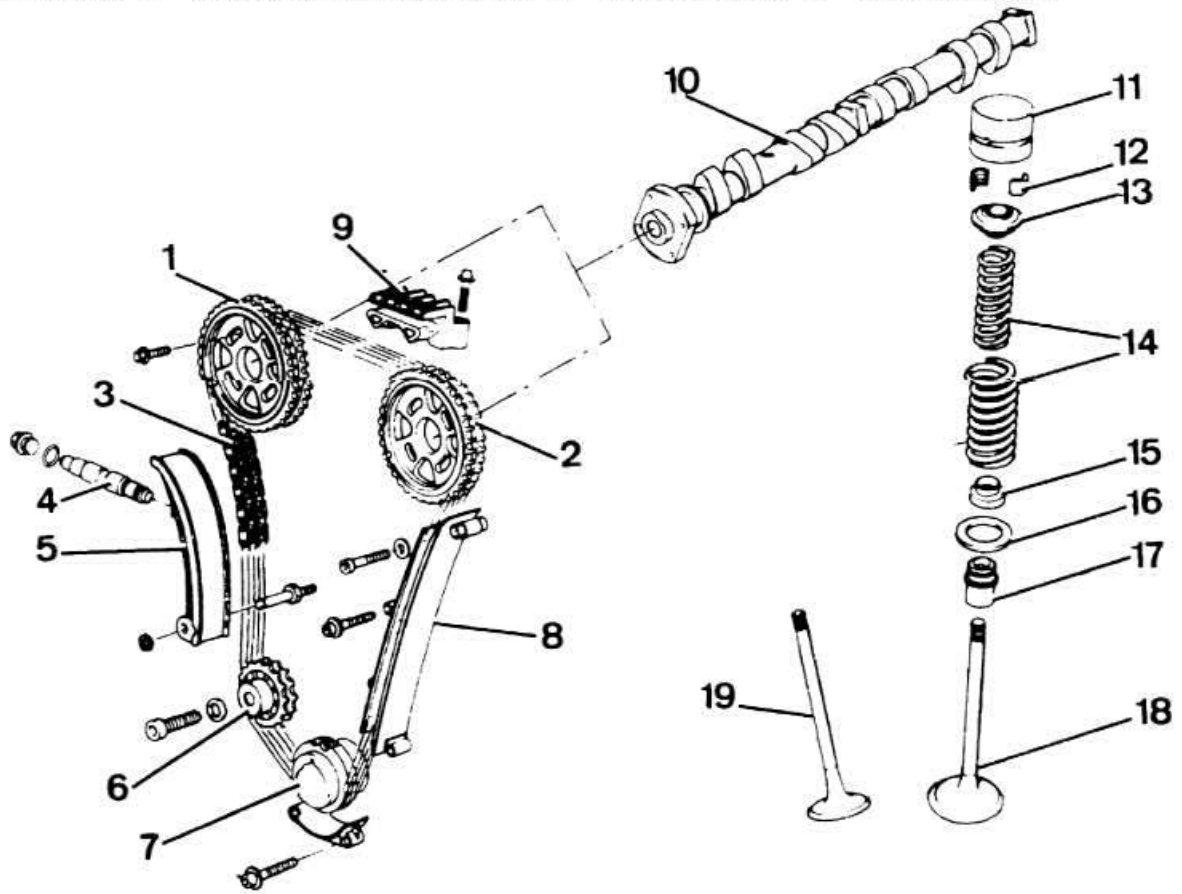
Привод механизма газораспределения двигателя М42:
